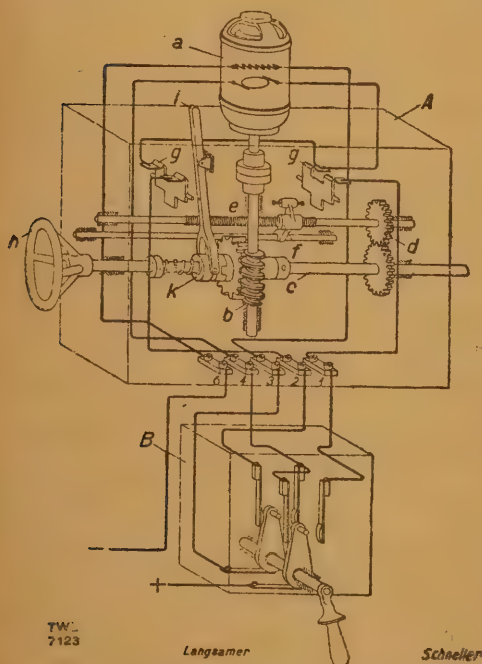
Schaltbild für Gleichstrom. A Drehzahlstellvorrichtung. B Umschalter, a Motor, b Schneckengetriebe, c Schneckenrad, d Handradwelle, e Getriebe zur Schaltspindel, f Schaltspindel, g Wandermutter, gg Endauschalter, h Handrad, i Kupplungshebel, k Kupplg.
